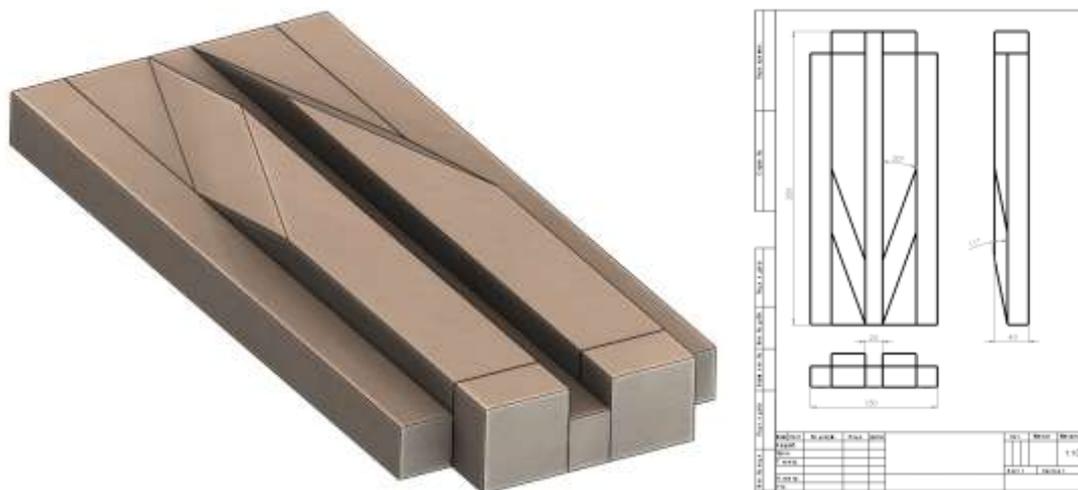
Модель и чертеж сборочной конструкции инструмента
